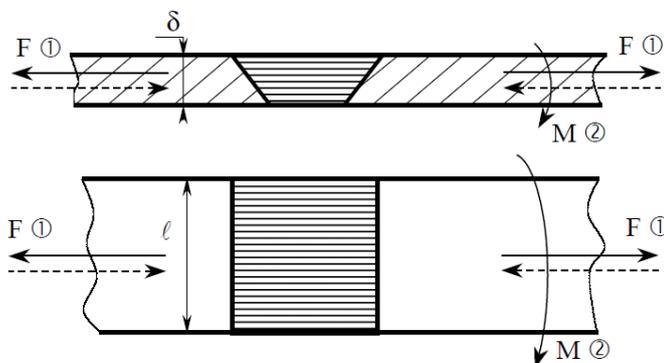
Виды нагружения стыковых сварных швов
